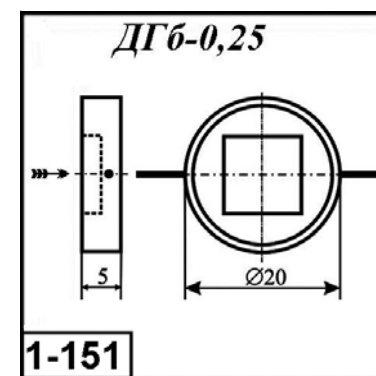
Внешний вид и габаритные размеры детектора типа ДГб-0,25
